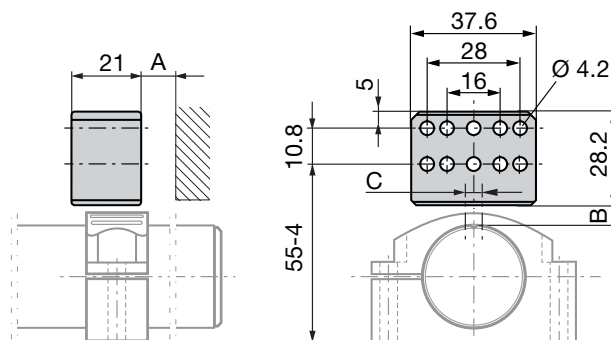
Dimensões e distâncias para o encoder de posição BTL6-A-3800-2
